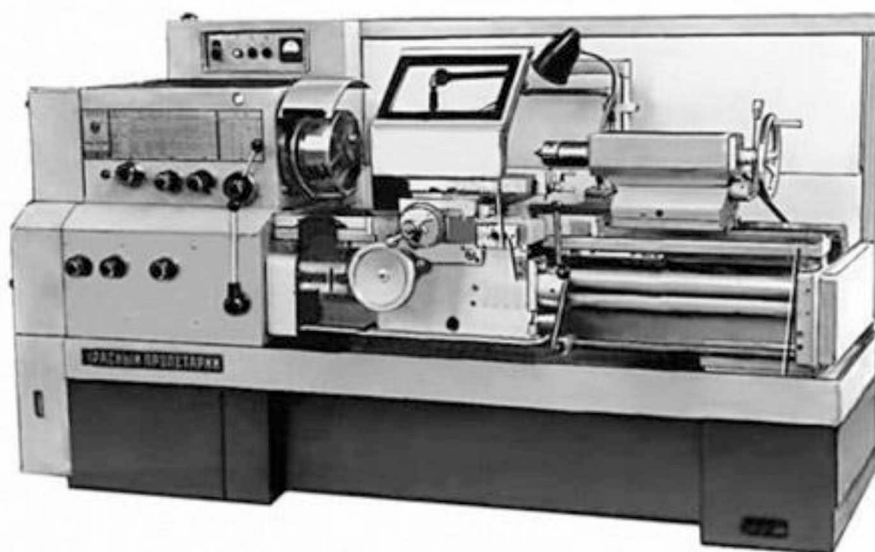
Загальний вид токарно-гвинторізного верстата 16K20
